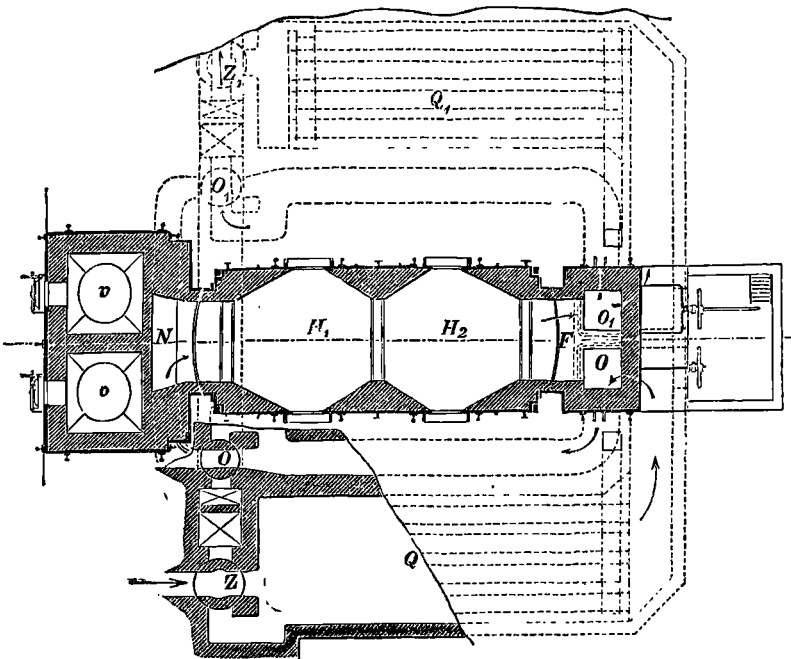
Four à puddler rotatif de Pietzka ; coupe horizontale.
